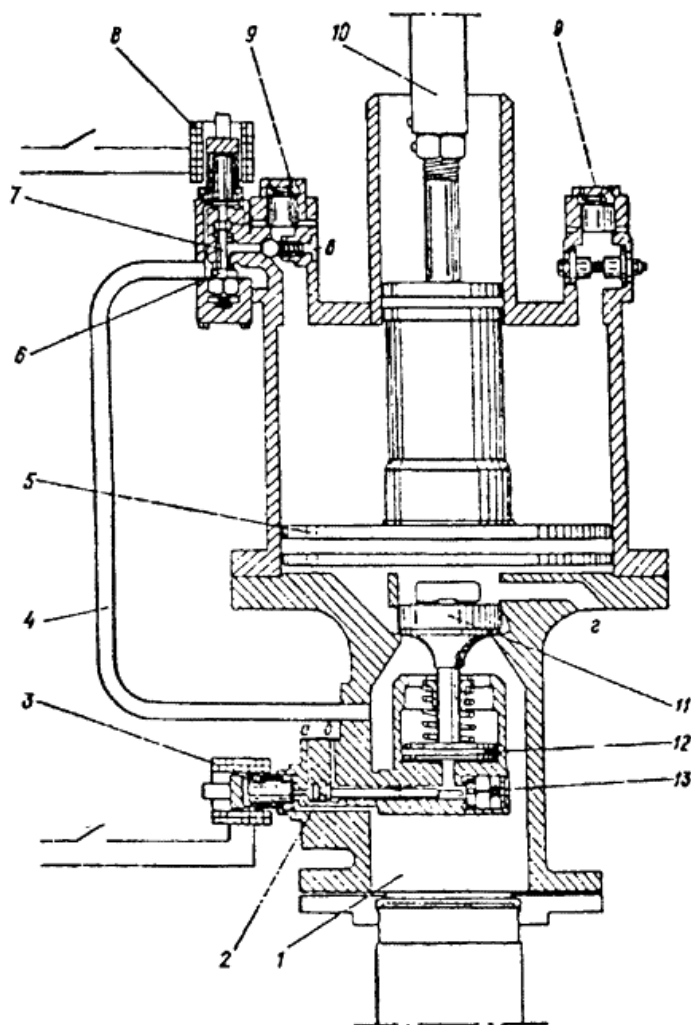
Силовий приводний пневматичний механізм для елегазового вимикача.
